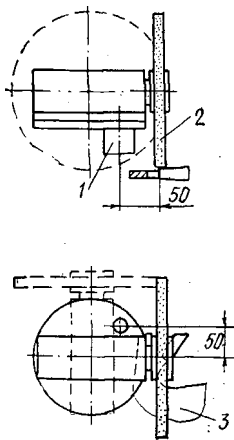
Схема боковой обработки зуба на устройстве конструкции Г. В. Паршева: 1 — ось качания круга; 2 — шлифовальный круг; 3 — обрабатываемый зуб пилы с пластинкой из твердого сплава
